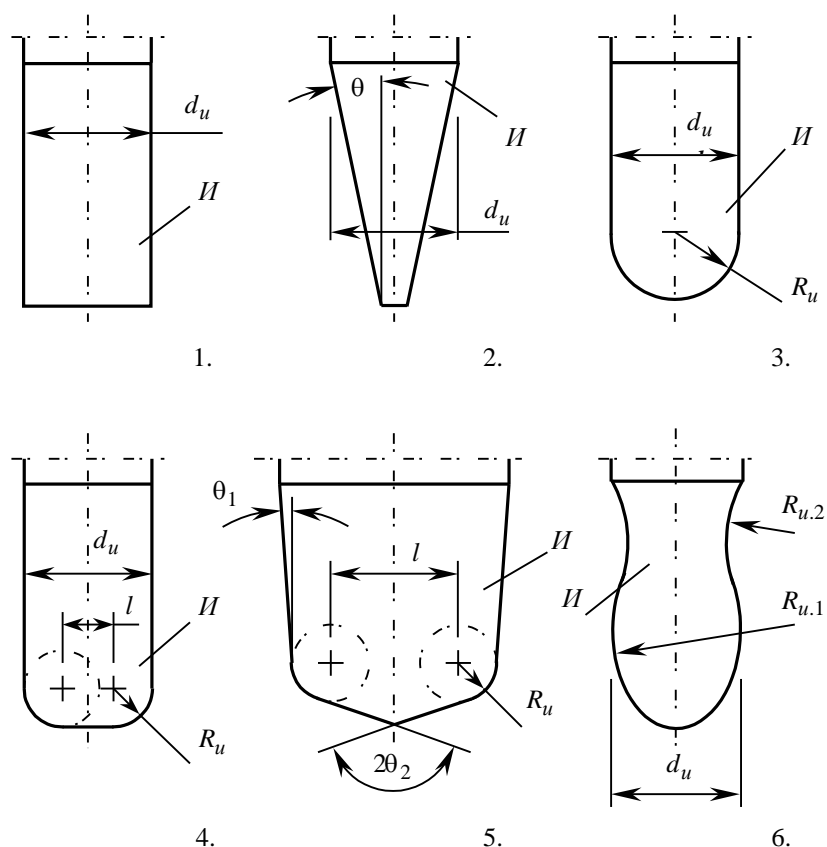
Режущие инструменты для обработки сложных поверхностей деталей на многокоординатных станках с ЧПУ: цилиндрический (1), конический (2), со сферической головкой (3), с тороидальной рабочей частью (4), АРТ (5), фасонный (6).
